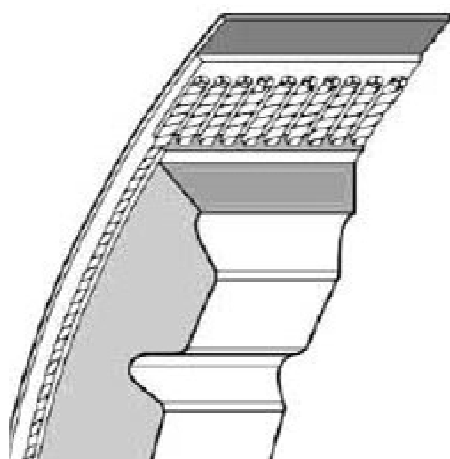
Клиновой узкий ремень с зубчатой кромкой без обертки боковых граней
